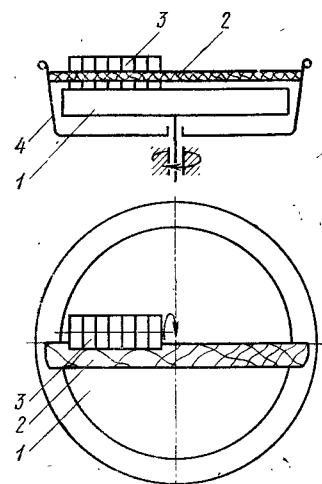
Кругление заготовок на станке типа ОС-320
